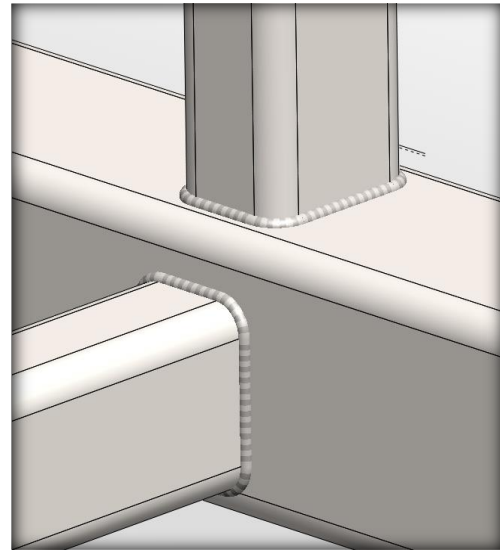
Detalle 3: Encuentro perfiles #80x60 con perfil parte inferior #120.
